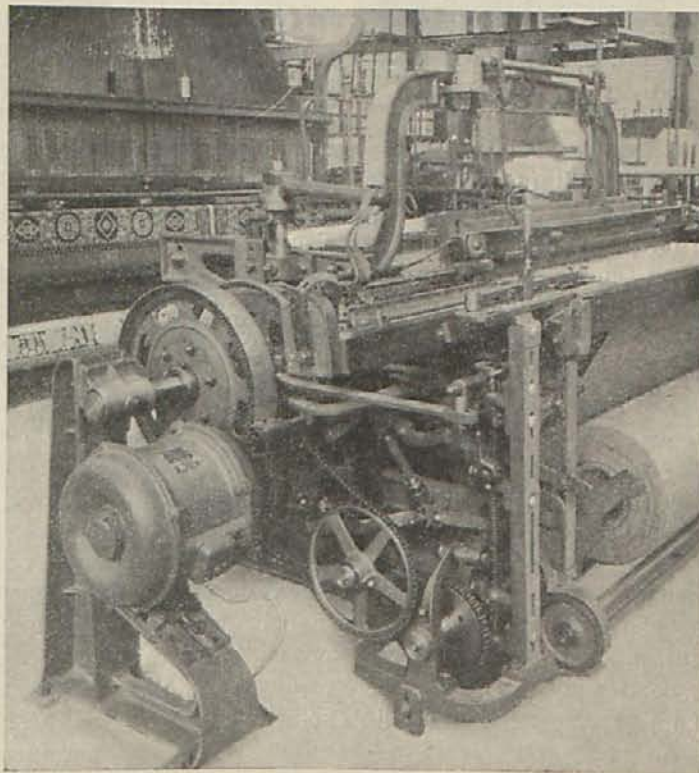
Transmissió per engranatges en un teler de bànoves
